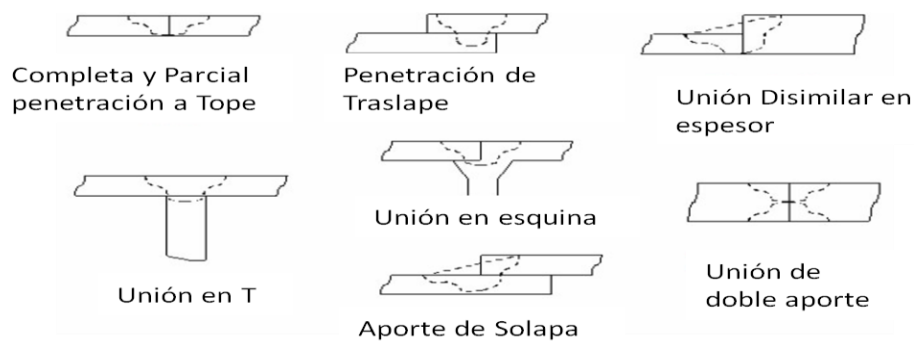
Proceso de soldadura FSW. [12]
